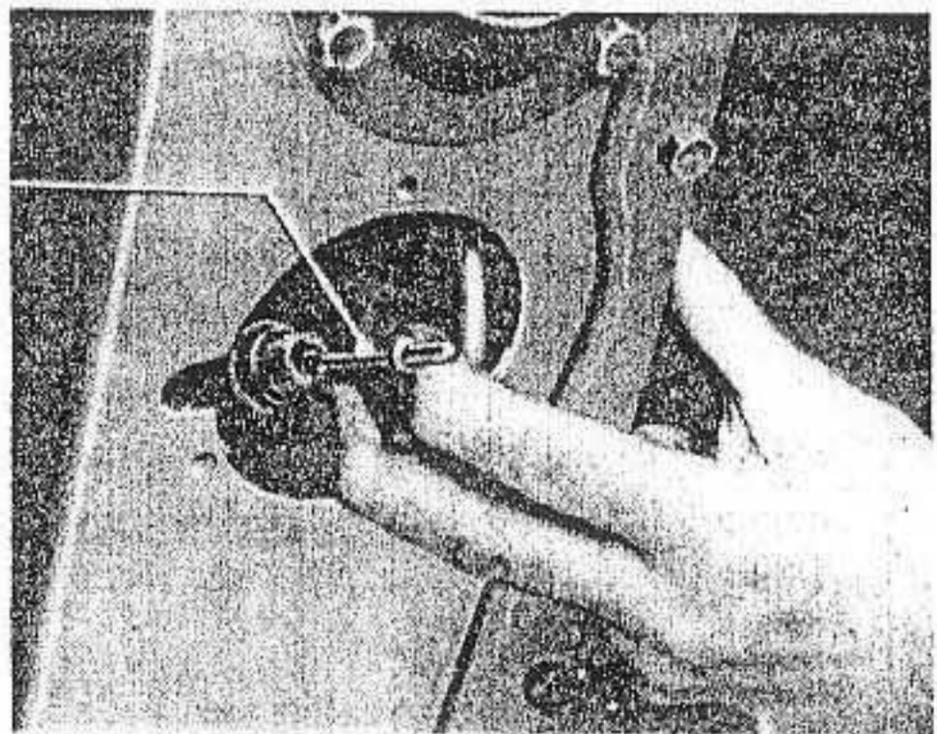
Comment ramener la soupape de refoulement sur son siège (pompe Lavalette).
